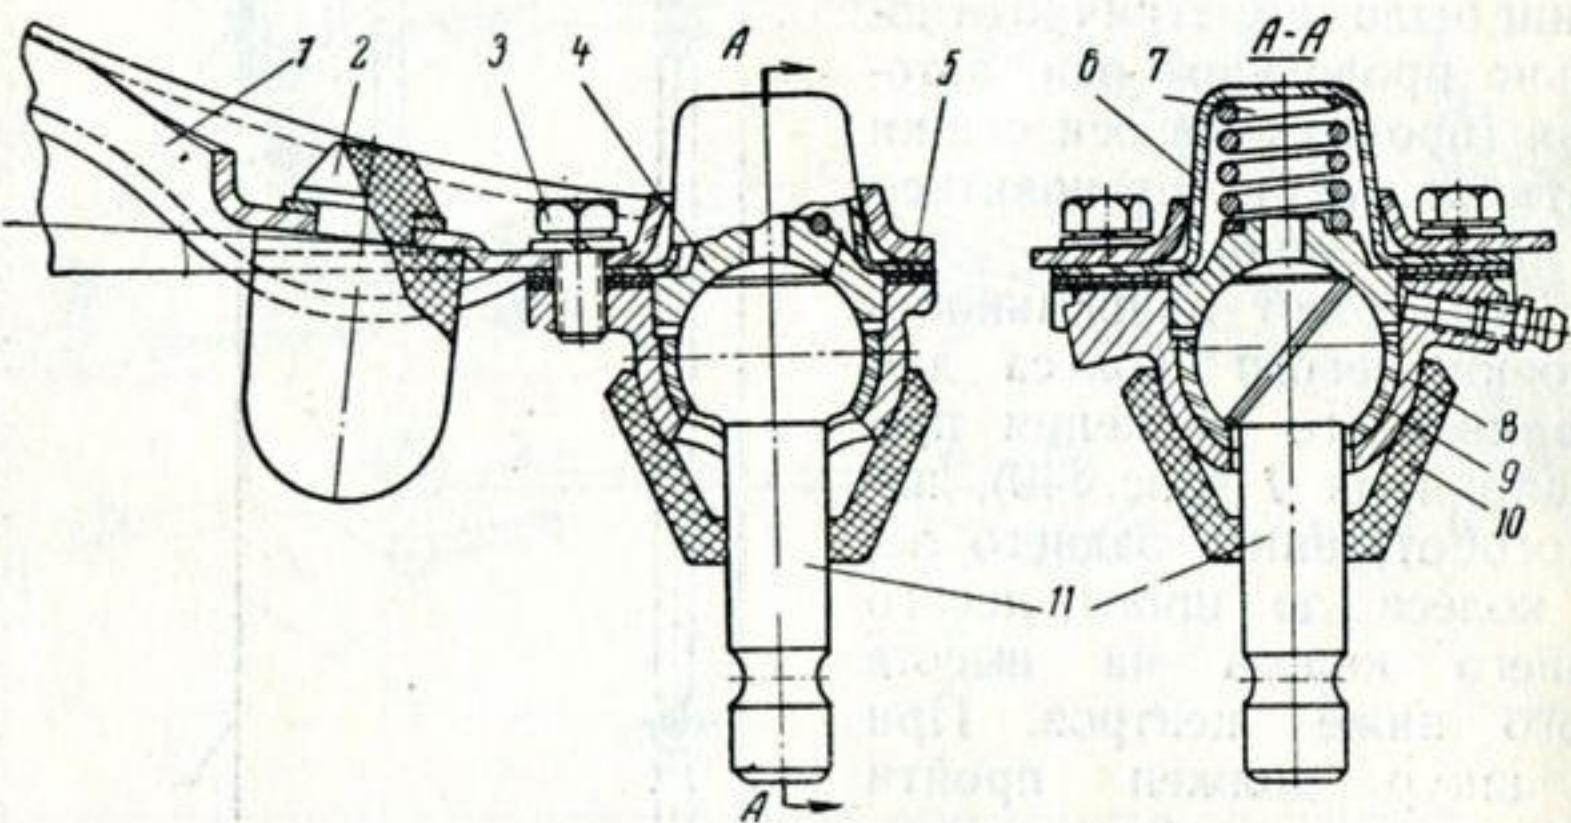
Верхний шаровой шарнир стойки подвески передних колес:
